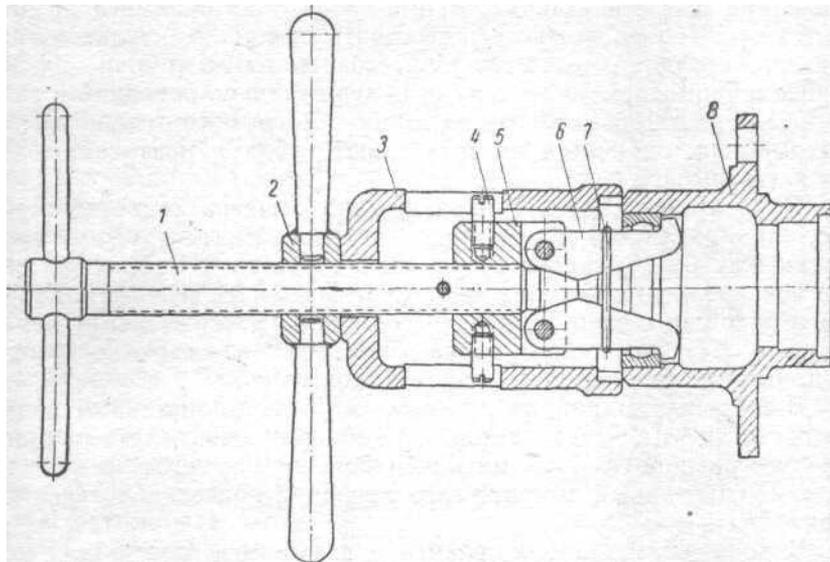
Съемник для выпрессовывания наружного кольца внутреннего подшипника ступицы переднего колеса:
